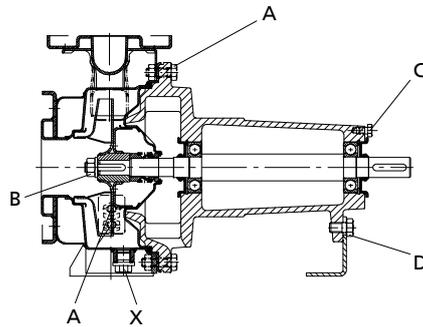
Позиции затяжки винтов диаметр рабочего колеса 125, 160, 200, кроме 50-200, 65-200, 80-200
